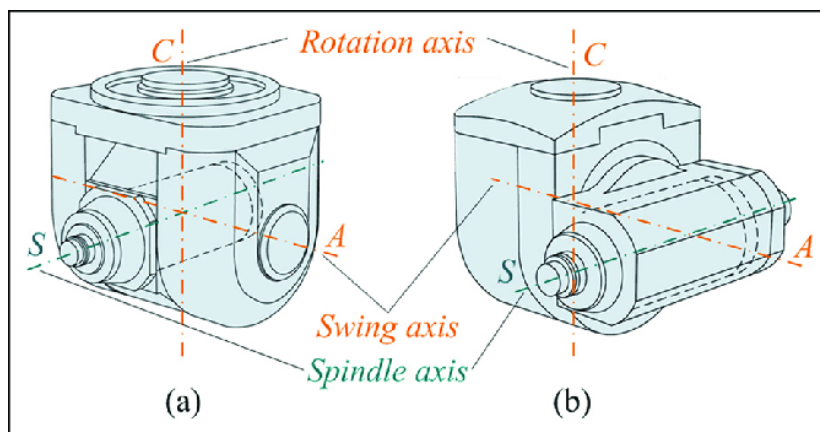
Двороторна фрезерна головка: (а) вилковий тип і (б) зміщений тип.
